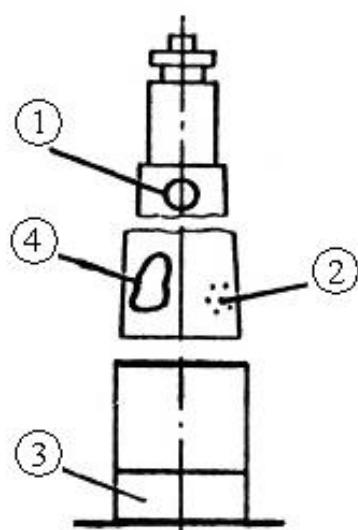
Дефекты котла водяного отопления, ремонтируемые сваркой или наплавкой
